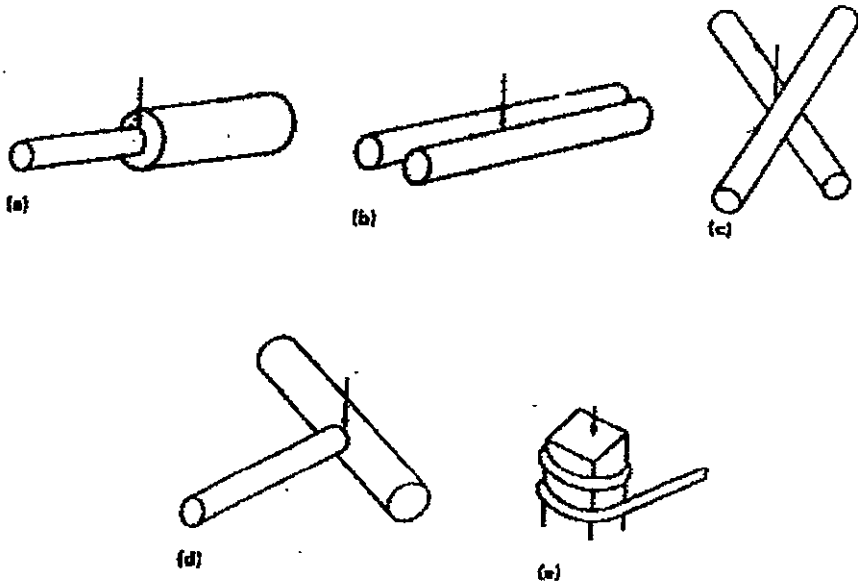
Diseño de uniones para soldar por haz de láser en alambre. Las flechas muestran la dirección del haz del láser (a)soldadura de tope.(b)soldadura lateral de perfiles circulares.(c)soldadura de cruz.(d)soldadura en T.(e)soldadura de terminal
